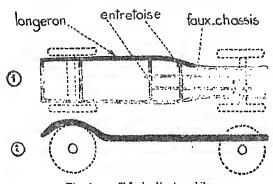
Chassis d'automobile. 1. Vue en plan. 2. Vue de profil.
